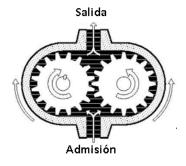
5. Bomba de engranaje de desplazamiento positivo
